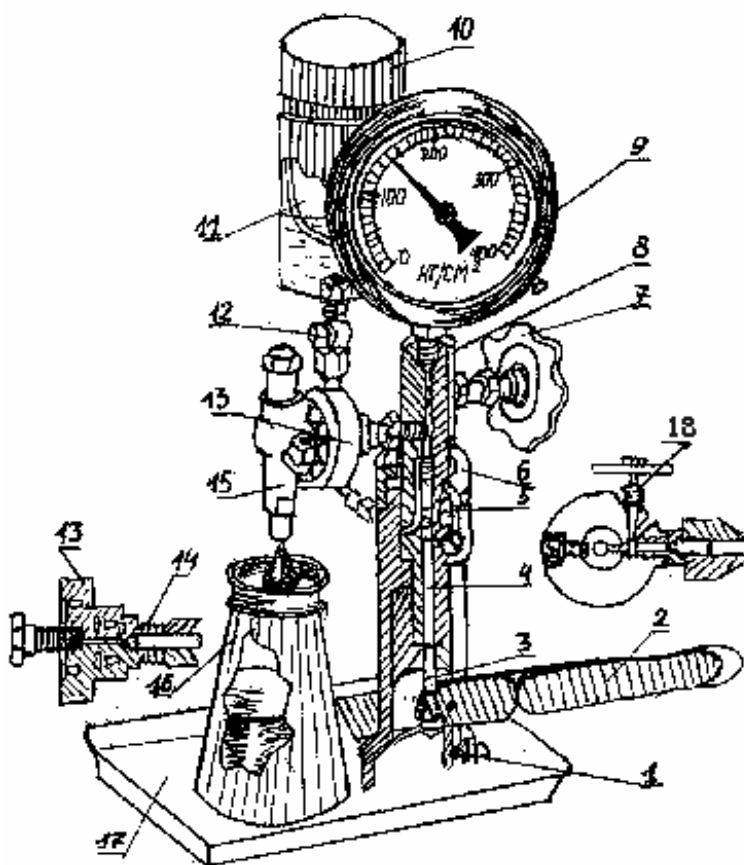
Прибор КП - 1609 А для испытания и регулировки форсунок:
